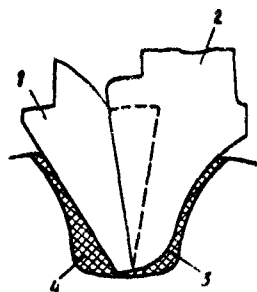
Распределение припуска при черновом нарезании зубьев стандартными и фасонными резцами
